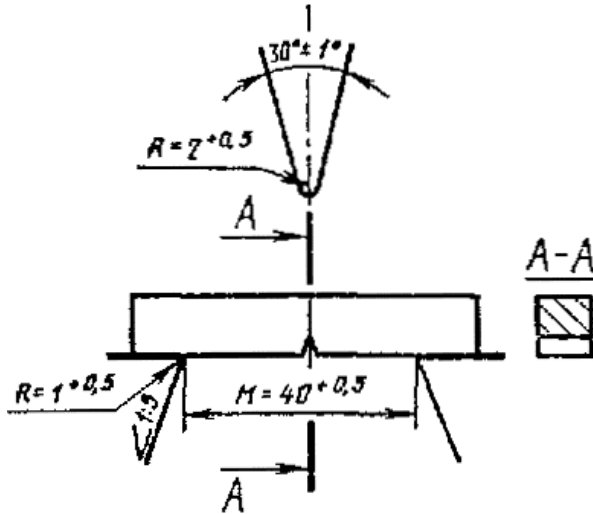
Ніж маятника й опори із установленим зразком
